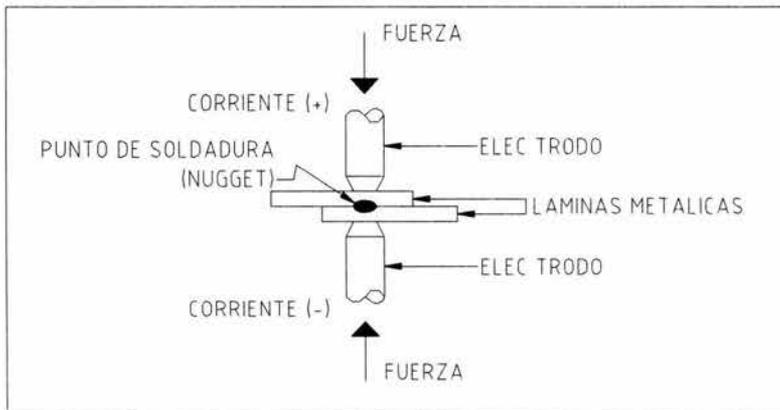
Principales componentes del proceso de soldadura por resistencia
